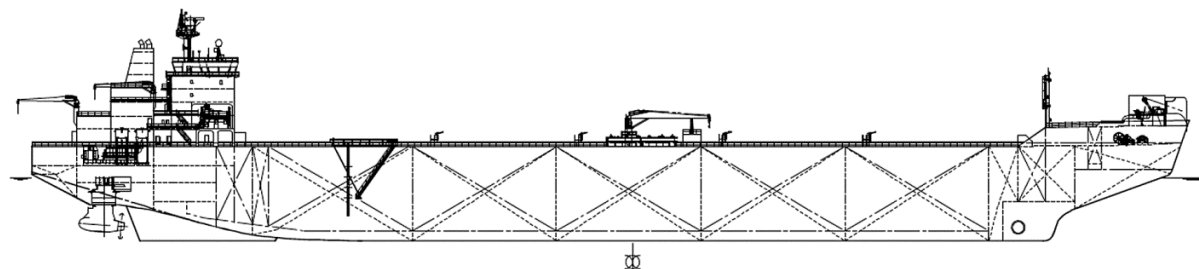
Боковой вид арктического челночного танкера двойного действия «Василий Динков»
